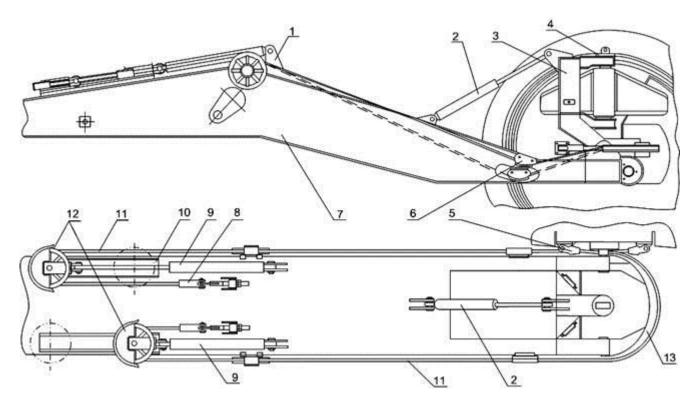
Приводы поворота и наклона ротора: 1 – кронштейн; 2 – гидроцилиндр наклона ротора; 3 – крестовой кронштейн; 4 – вертикальная ось; 5, 8 – коуши; 6, 13 – направляющие; 7 – стрела ротора; 9 – гидроцилиндр поворота ротора; 10 – опора с направляющей; 11 – канат; 12 – блок подвижный
